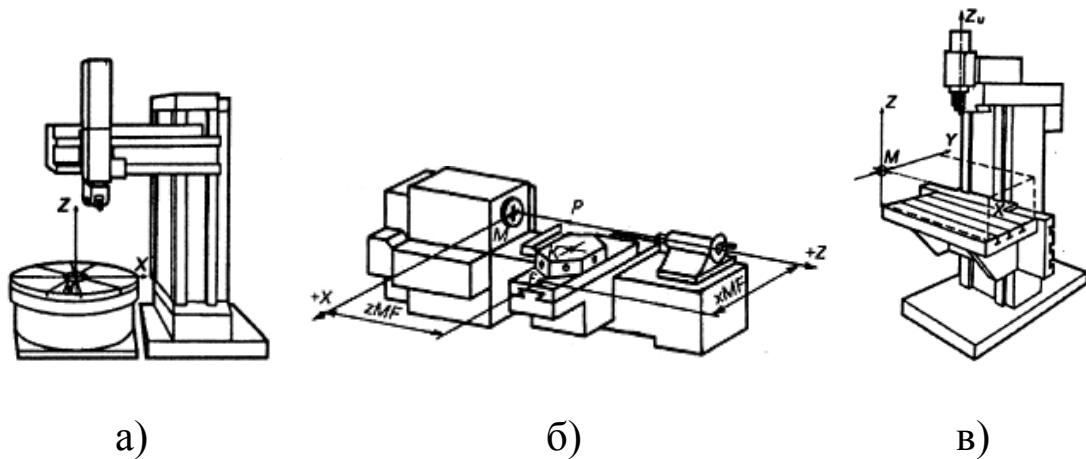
Размещение координатных систем у различных станков с ЧПУ: а) карусельный; б) токарный, в) вертикально-фрезерный
